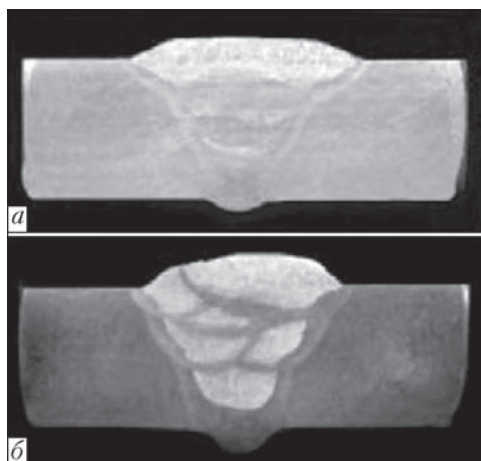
Макрошлиф стыкового сварного соединения: а — сварка методом «один слой за один проход»; б — сварка точными валиками
